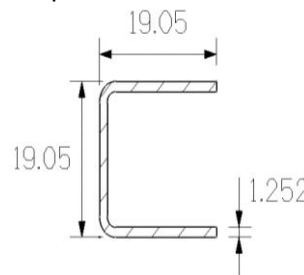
Perfil estructural optimizado (Acotación en mm).
